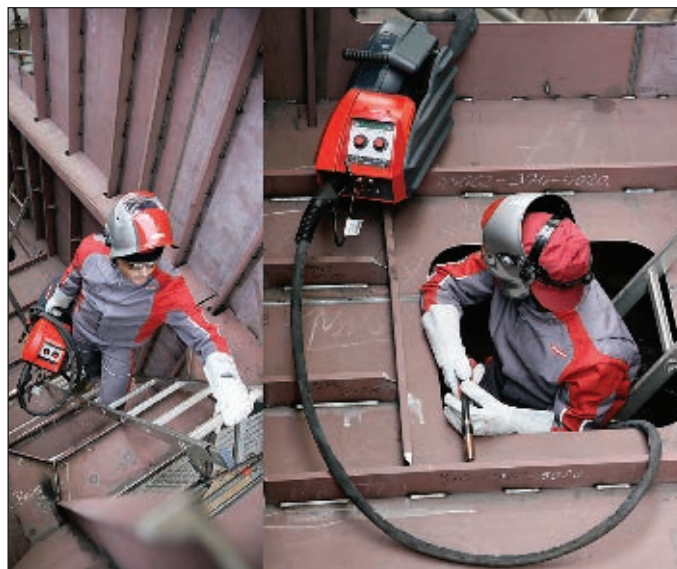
Устройство подачи проволоки массой 12 кг с дисплеем управления и горелкой может быть легко перенесено в труднодоступные места для выполнения сварки
